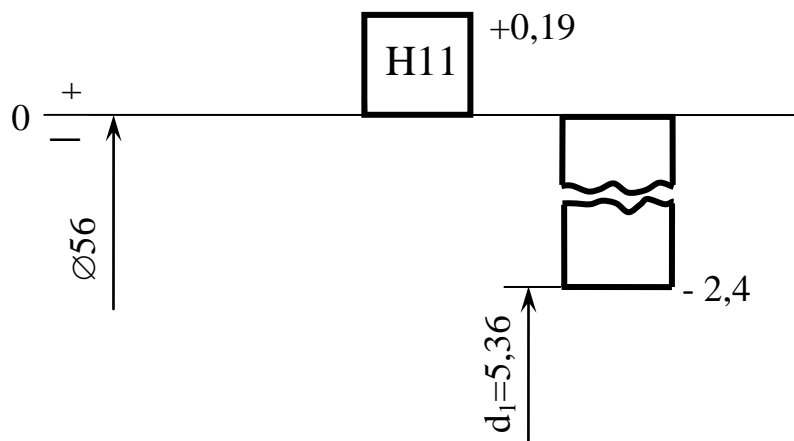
Схема розташування полів допусків шліцьового з'єднання $8 \times 56 \times 62$ за розміром d при центруванні за D або b
